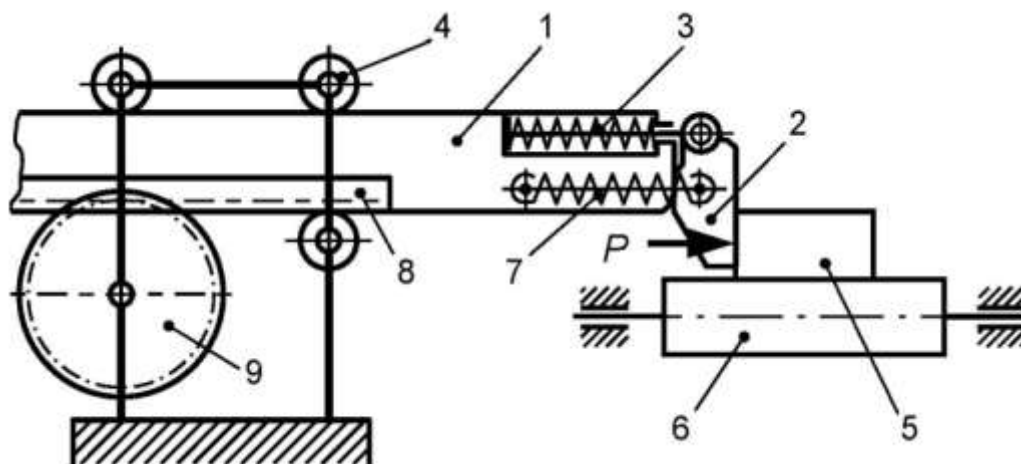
Схема реечного толкателя: 1 - толкающая штанга; 2- толкающие пальцы; 3- пружинные амортизаторы; 4 - опорные катки; 5 - блюм; 6 - рольганг; 7 - замыкающая пружина; 8 - зубчатая рейка; 9 - приводная шестерня
